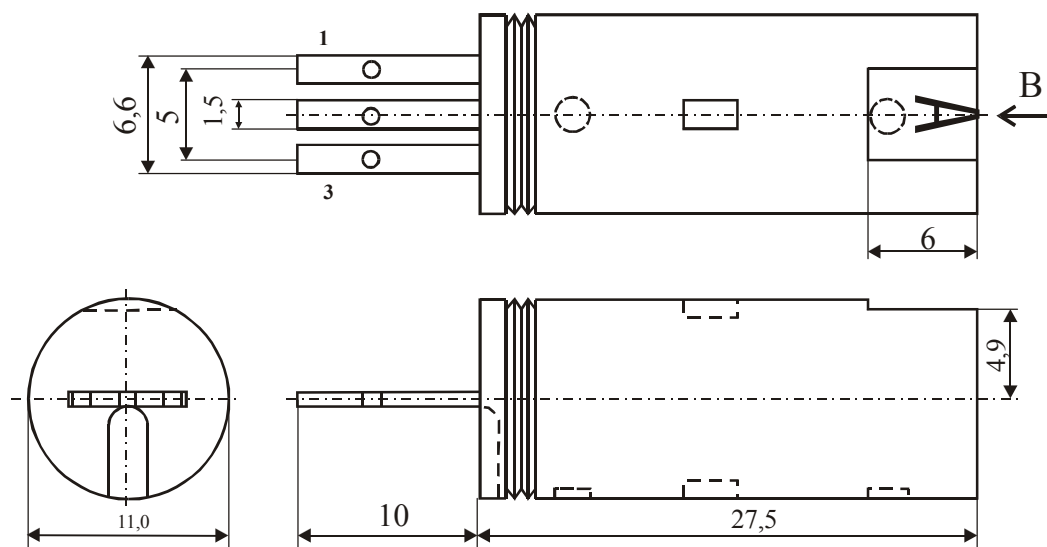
Внешний вид и габаритные размеры датчиков типа ATS610LSC и ATS632LSC
